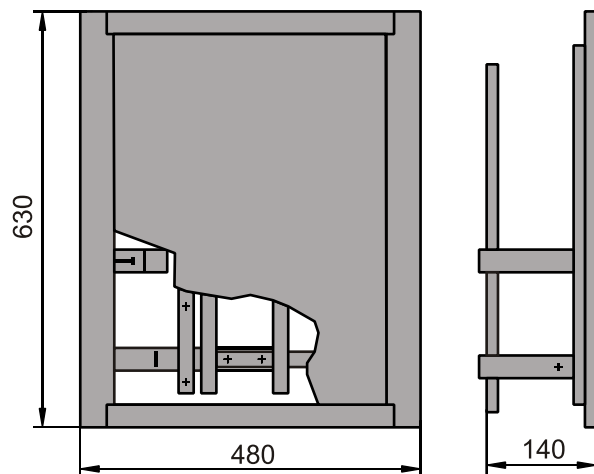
Внешний вид и габаритные размеры ЩК1109-02
